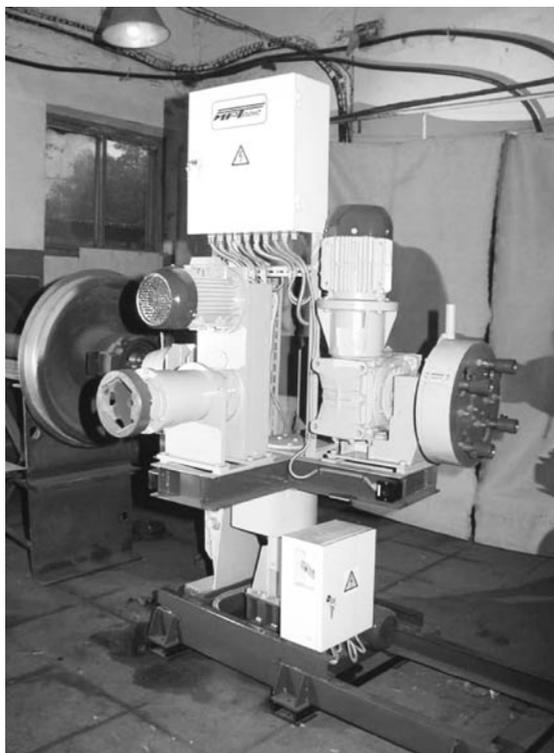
Общий вид станда для демонтажа буксовых узлов
